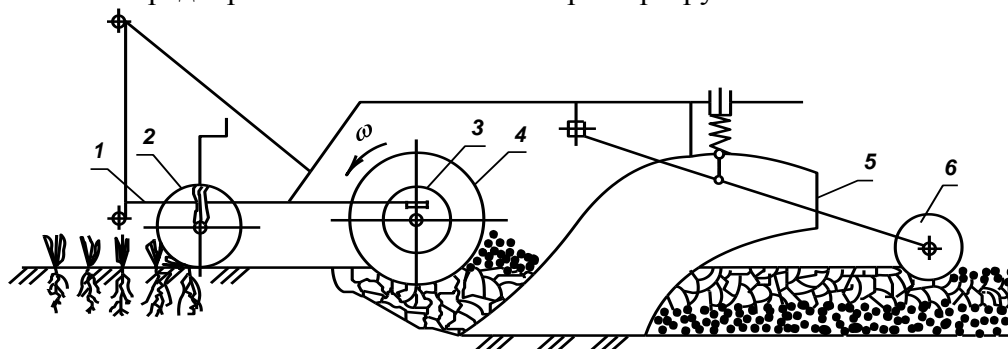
Схема комбинированного плуга для гладкой безбороздной вспашки с активными и пассивными рабочими органами.
